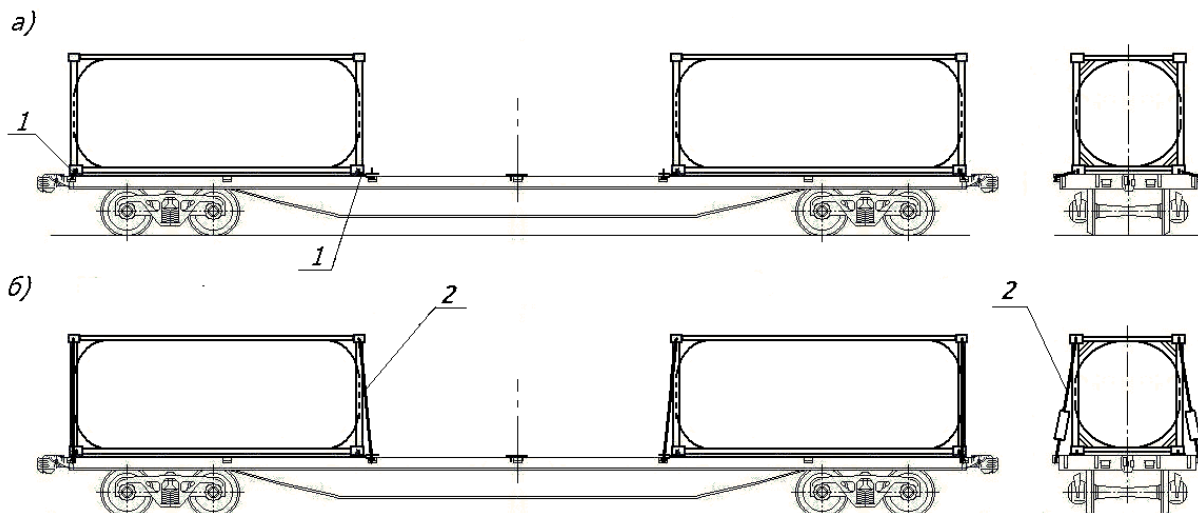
Дополнительное крепление контейнеро-цистерн на платформе для крупнотоннажных контейнеров:
